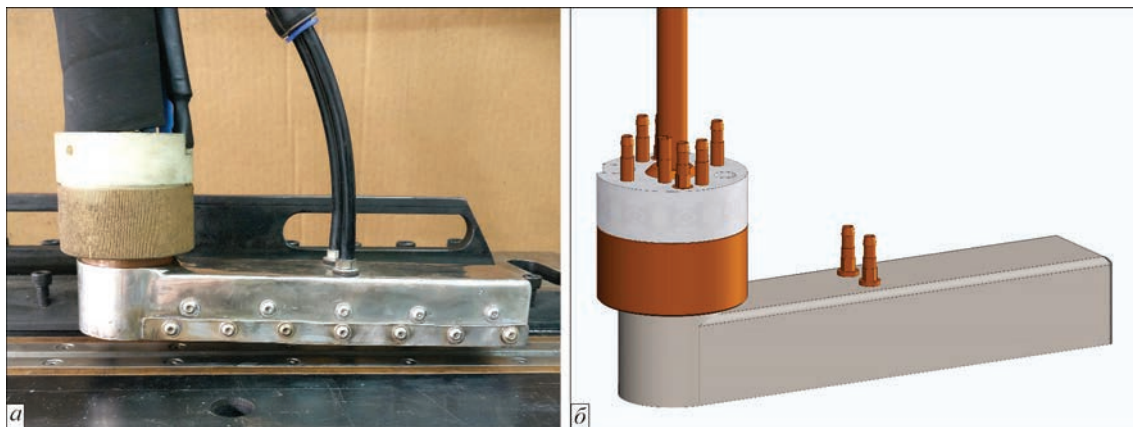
Внешний вид (а) и схема (б) горелки для роботизированной гибридной плазменно-дуговой сварки с дополнительным защитным соплом
